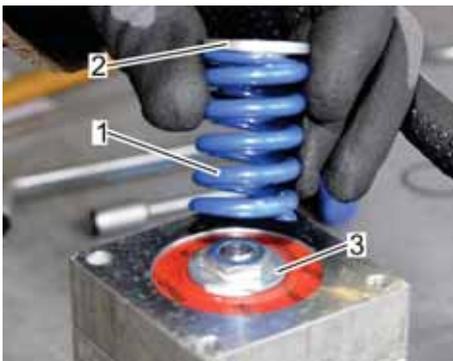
Sollwertfeder mit Federteller aufsetzen
